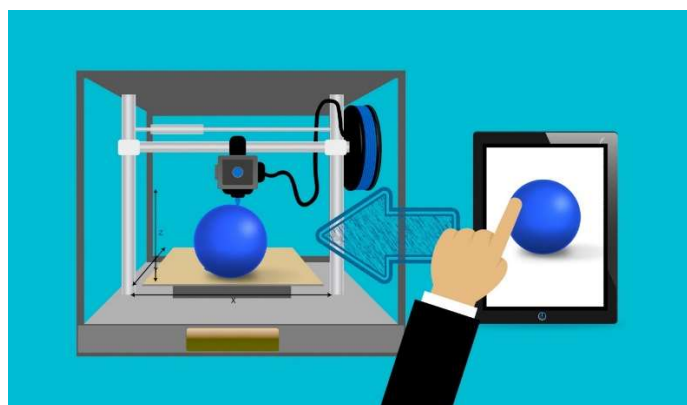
Impressão de um objeto a partir de um ficheiro CAD
